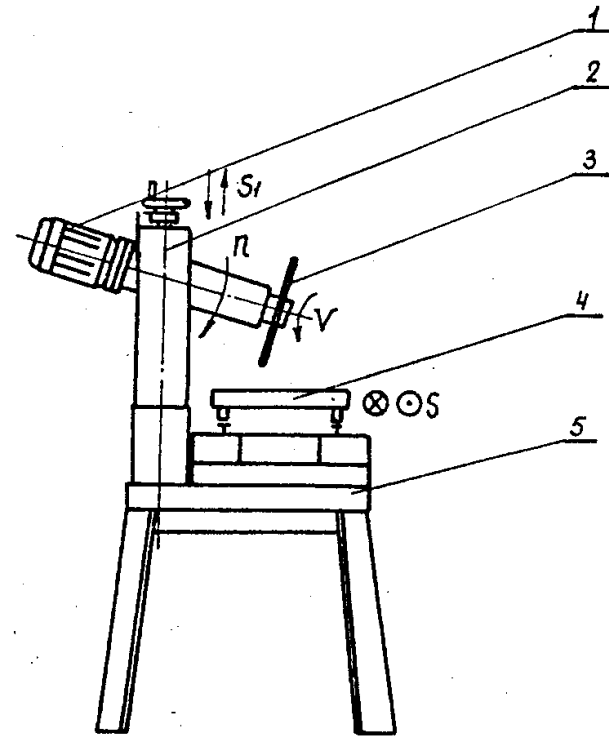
Переносный фрезерно-окантовочный станок:
